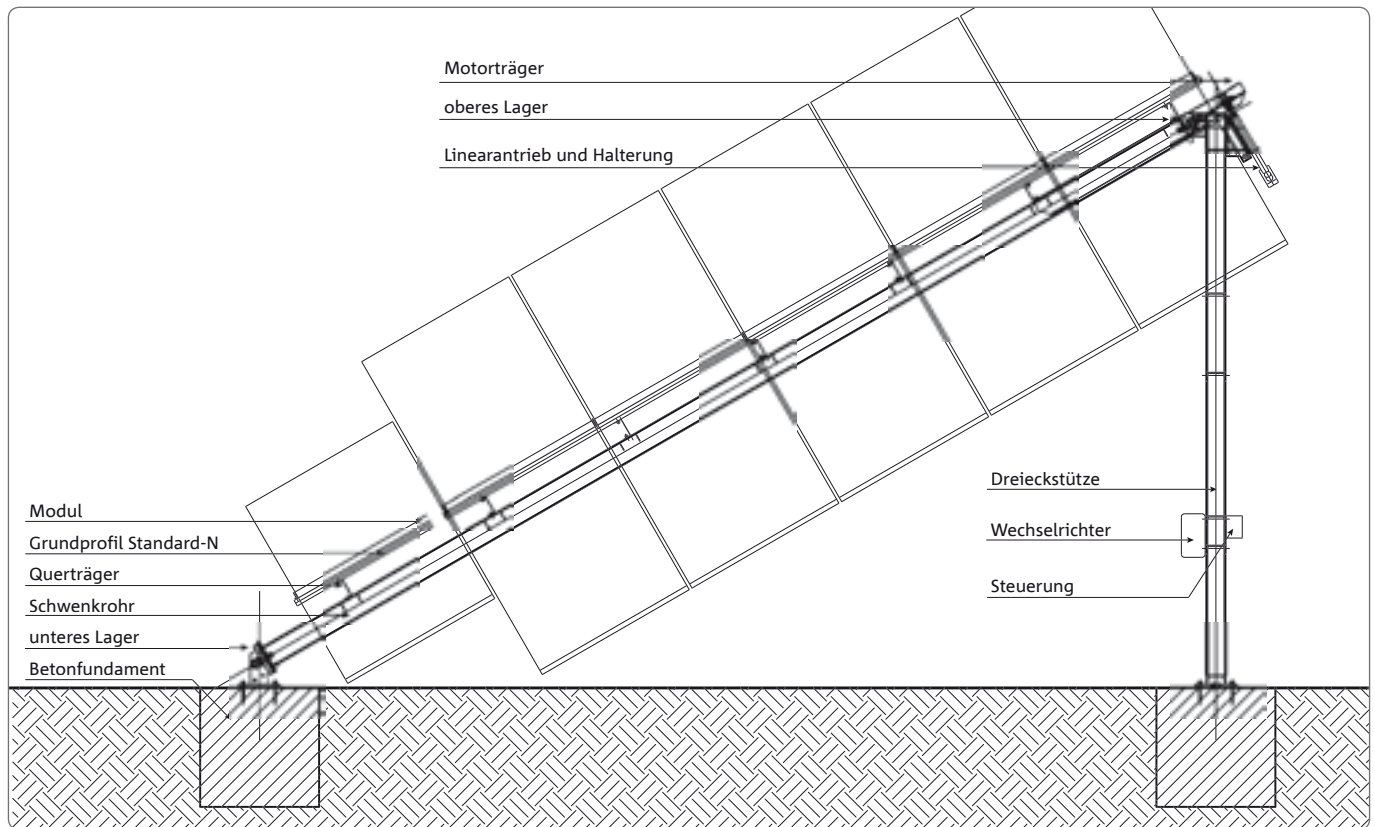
Hauptbaugruppen/ Übersichtszeichnung
